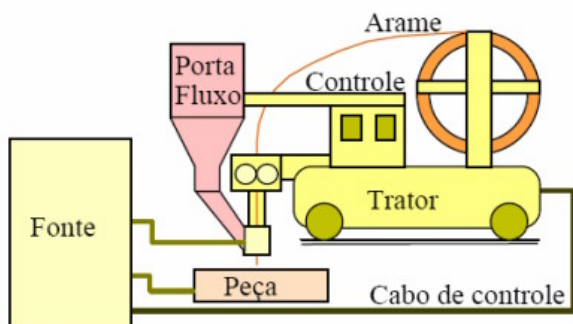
Esquema de soldagem a arco elétrico por arco submerso.
